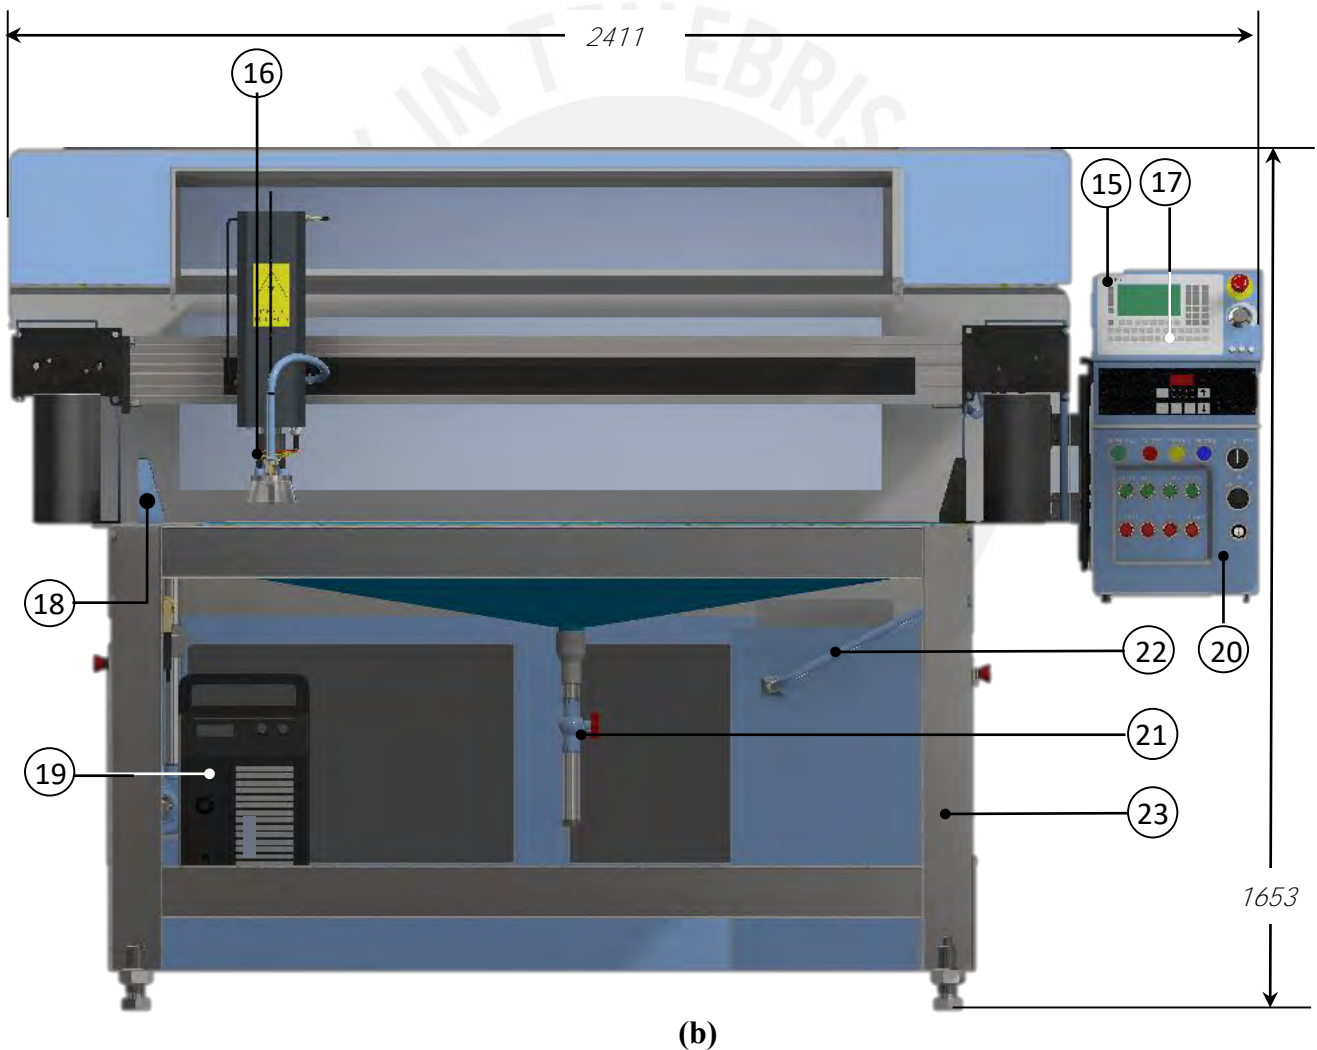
Sistema integrado (b) Vista frontal Fuente Plano E0-A0: Elaboración propia
